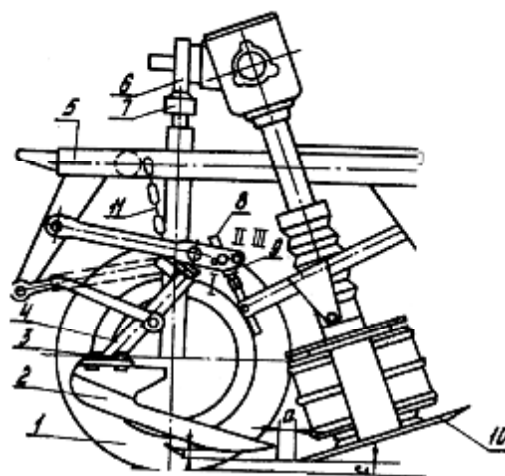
Регулювання гичкозрізального апарату машини БМ-6Б: 1 – копіювальне колесо; 2 – копір; 3,9 – гайка; 4 – стійка; 5 – рама; 6 – головка гвинта; 7 – гайка ковпачка; 8 – тяга; 10 – ніж; 11 – ланцюг: а – горизонтальний зазор між ножем і копіром; в – вертикальний зазор між ножем і копіром; с – зазор між ножем і поверхнею поля
